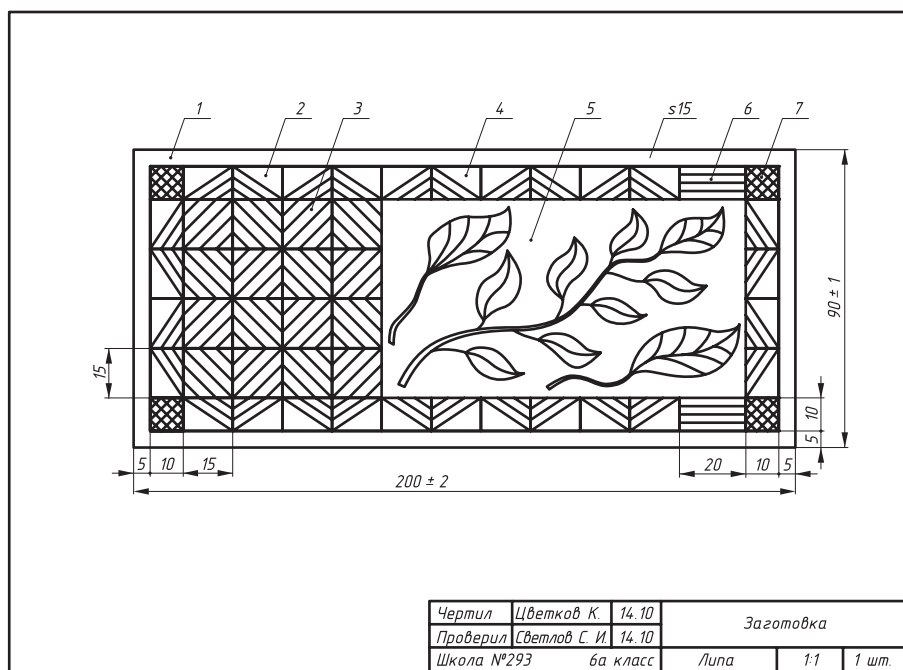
Чертёж заготовки: 1 — контурное поле;
